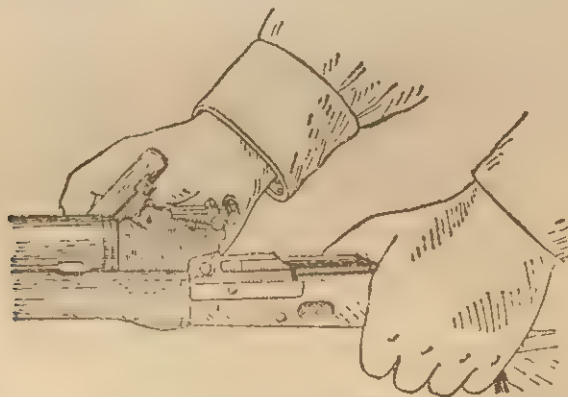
Поворот замыкателя газовой трубки с помощью пенала принадлежности
